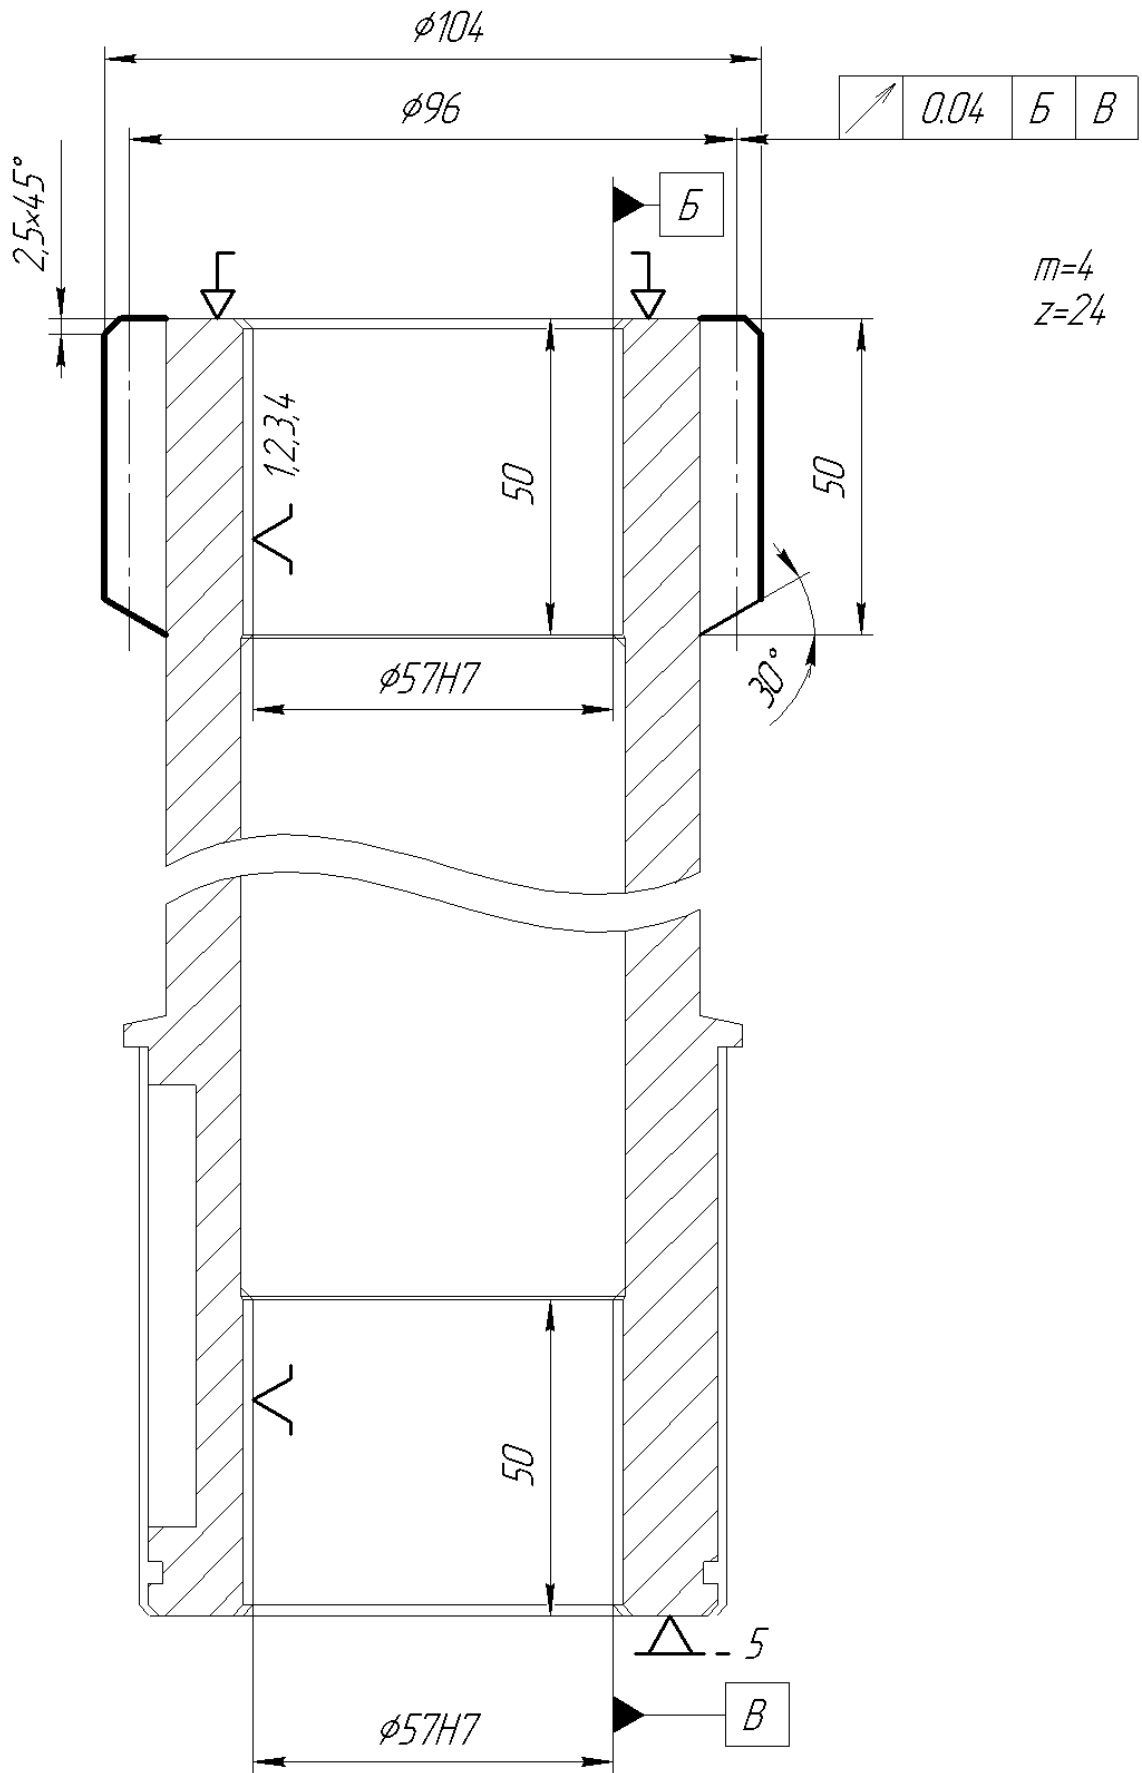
Схема базування і закріплення на операції 025 «Зубофрезерна»
